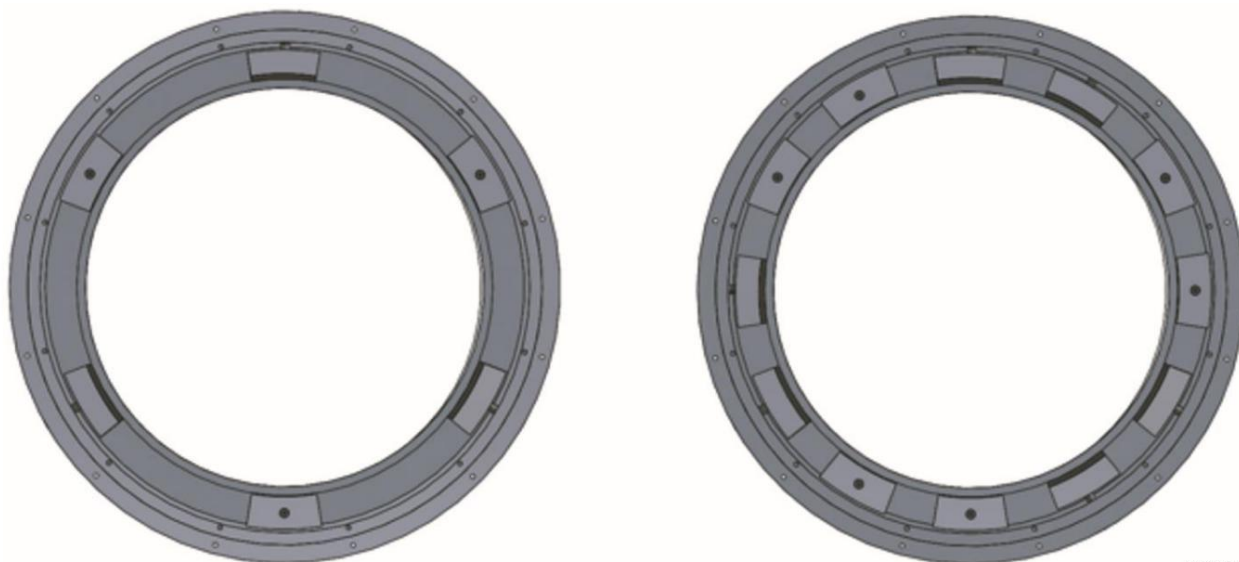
Окончательный вариант конструкции двигателя с приводом от обода, включающий конструкцию с воздушным подшипником (внутренний диаметр 14 дюймов и наружный диаметр 17 дюймов).
